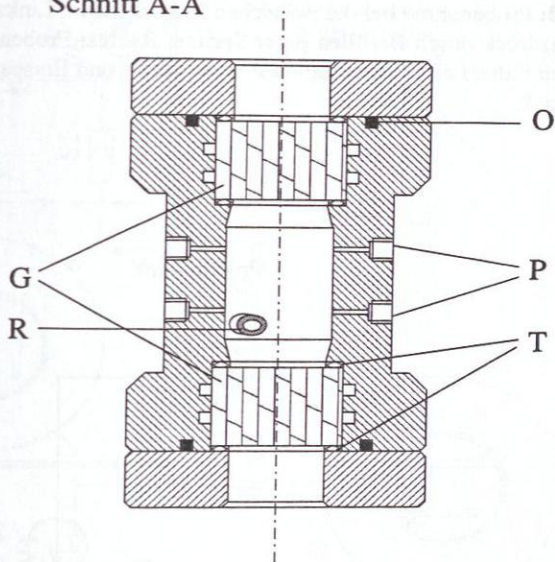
Schnitt durch die verwendete Hochdrucksichtzelle; G = Schaugläser aus Borosilikat, R = Röhrchen zur Aufnahme des Thermometers, O = O-Ring aus FEP-ummanteltem Viton, P = Bohrungen zur Probenahme, T = PTFE-Ringe
